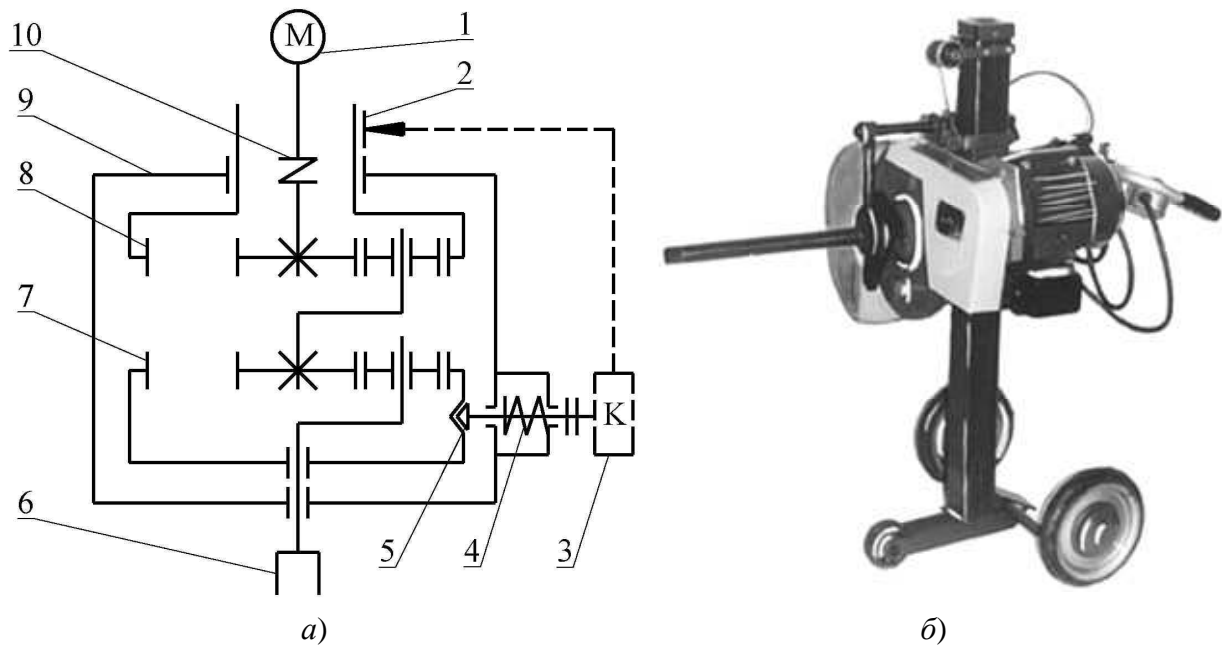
Схема (а) и общий вид (б) электромеханического гайковерта: 1 – электродвигатель; 2 – тормоз колодочный; 3 – конечный выключатель; 4 – пружина; 5 – конический стержень; 6 – шпиндель; 7 и 8 – колеса корончатые; 9 – корпус; 10 – муфта
